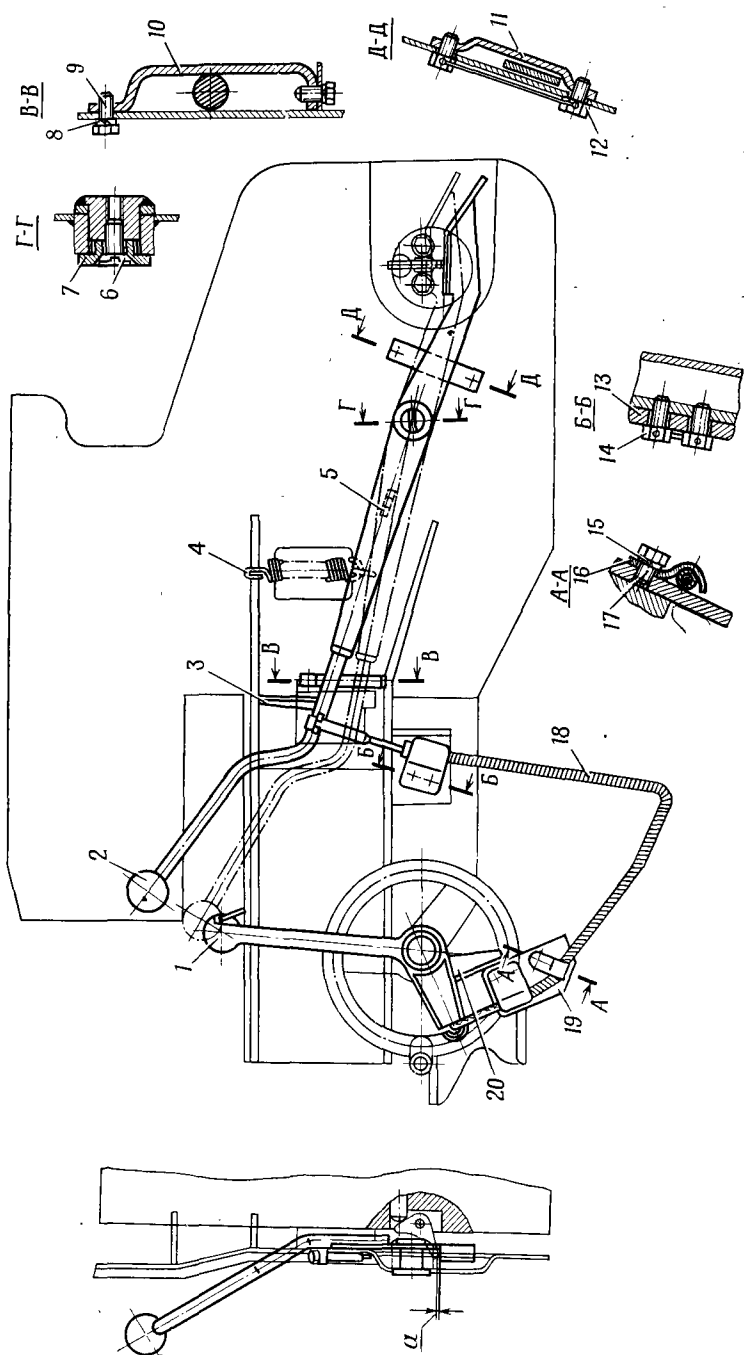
Полуавтоматика затвора Сб 30 — механизмы открывающий и закрывающий:
